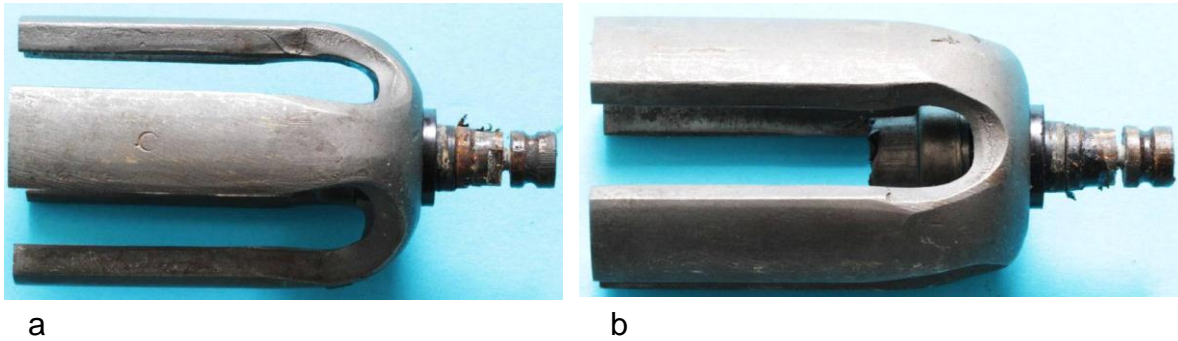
Vierpoliges Erregersystem mit Spurlager und Kabelanschluss: a) Gestempelter Magnetschenkel, b) Blick durch die Pollücke
